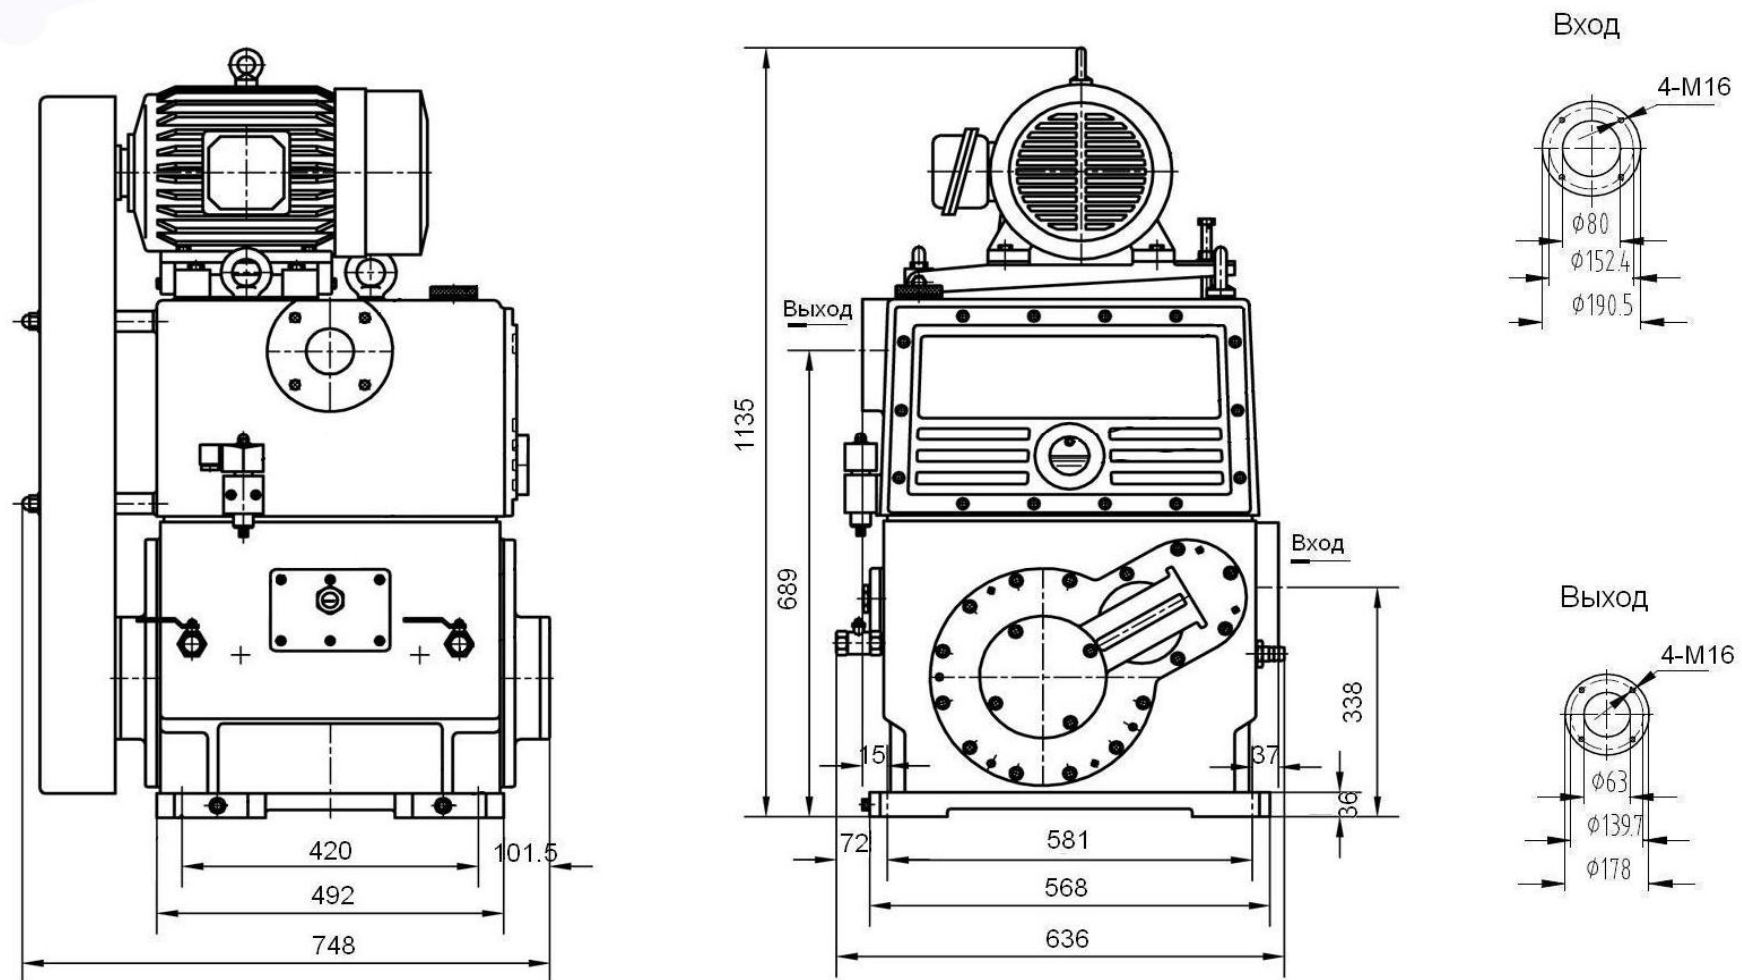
АВПЗ-80Д Агрегат вакуумный плунжерный
